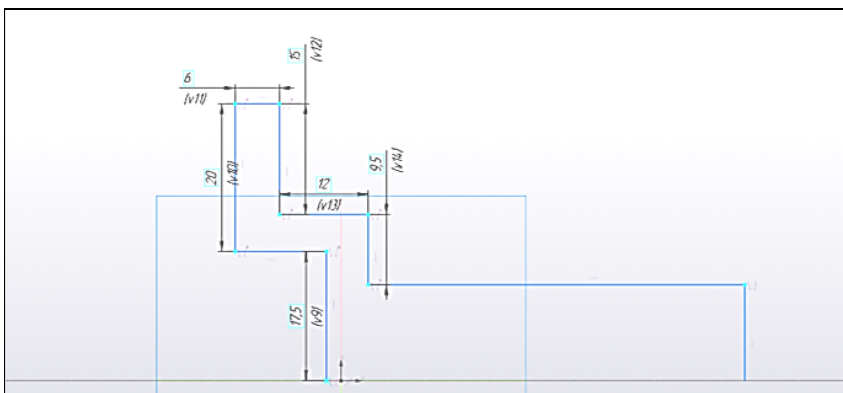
Эскиз вала с фланцем в ПК «КОМПАС-3D»
